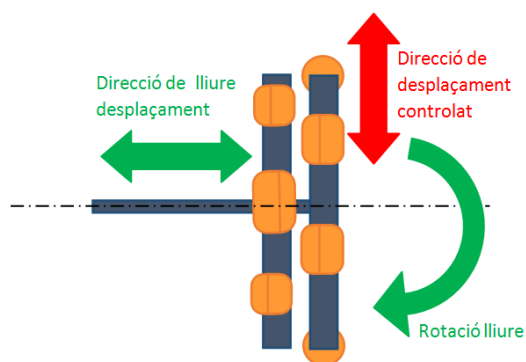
Esquema del conjunt de moviments controlats i lliure de les rodes amb corró perpendiculars a l'eix de la roda.
